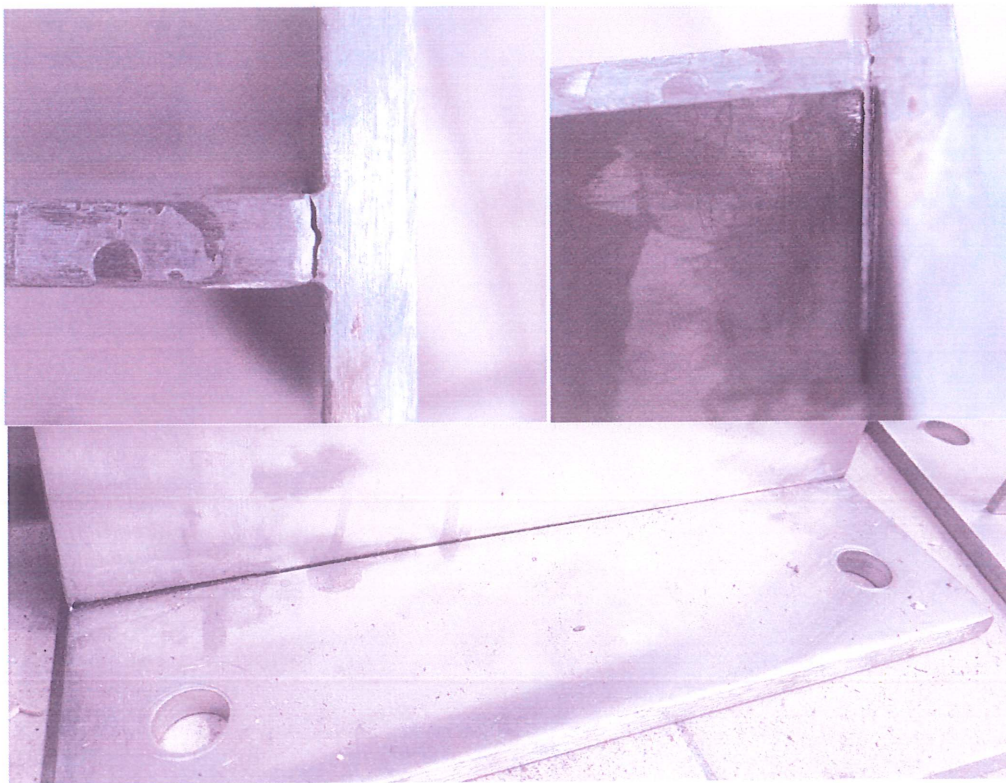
Характер разрушения сварного шва консоли Тип 4
